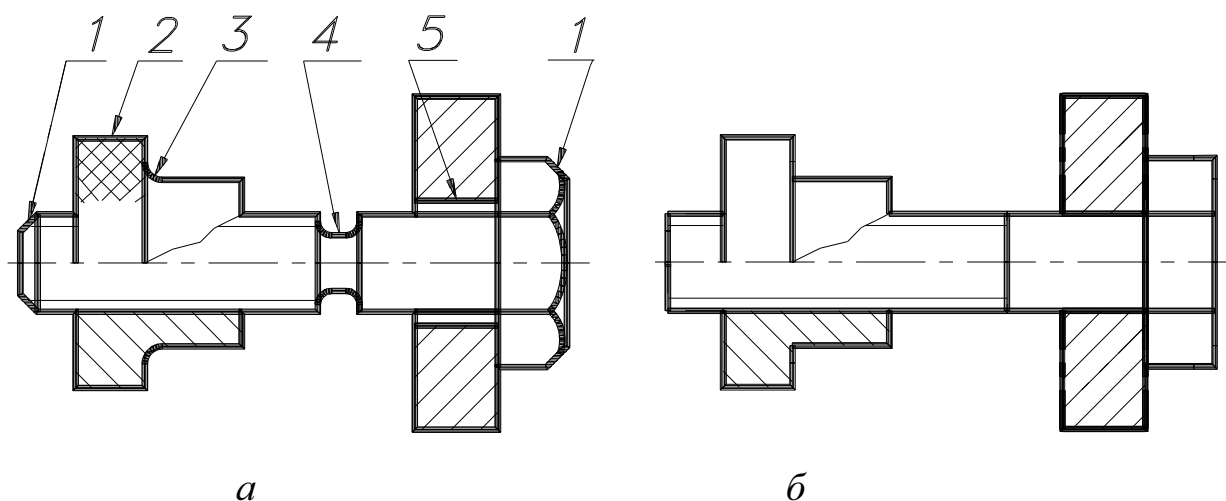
а* – полное вычерчивание деталей с мелкими элементами: фаска (1), накатка (2), скругление (3), проточка (4), зазор (5);
